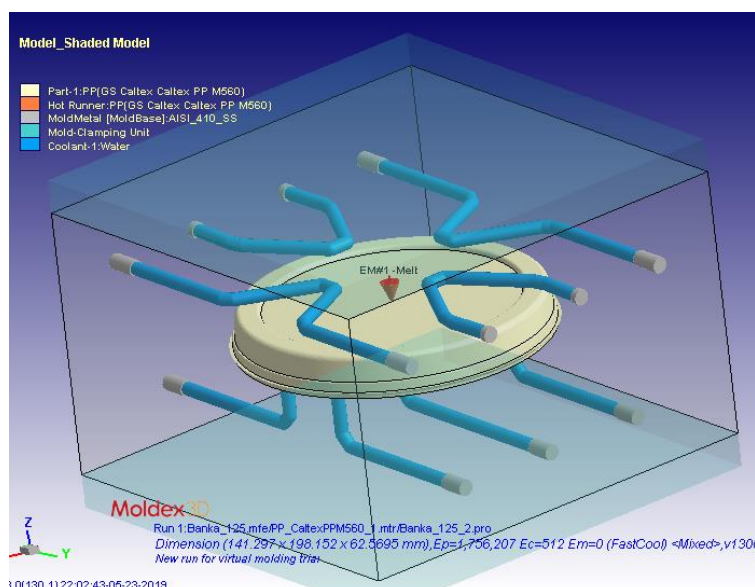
Модель пресс-формы для изготовления детали типа «Крышка тары»
